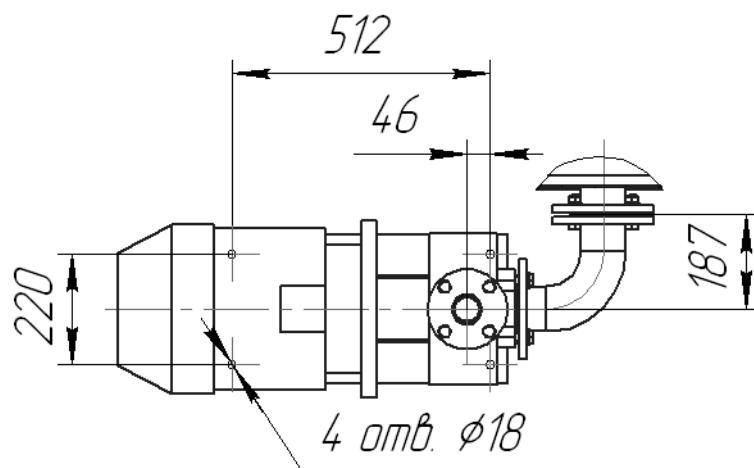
Схема установки анкерных болтов для крепления насоса
